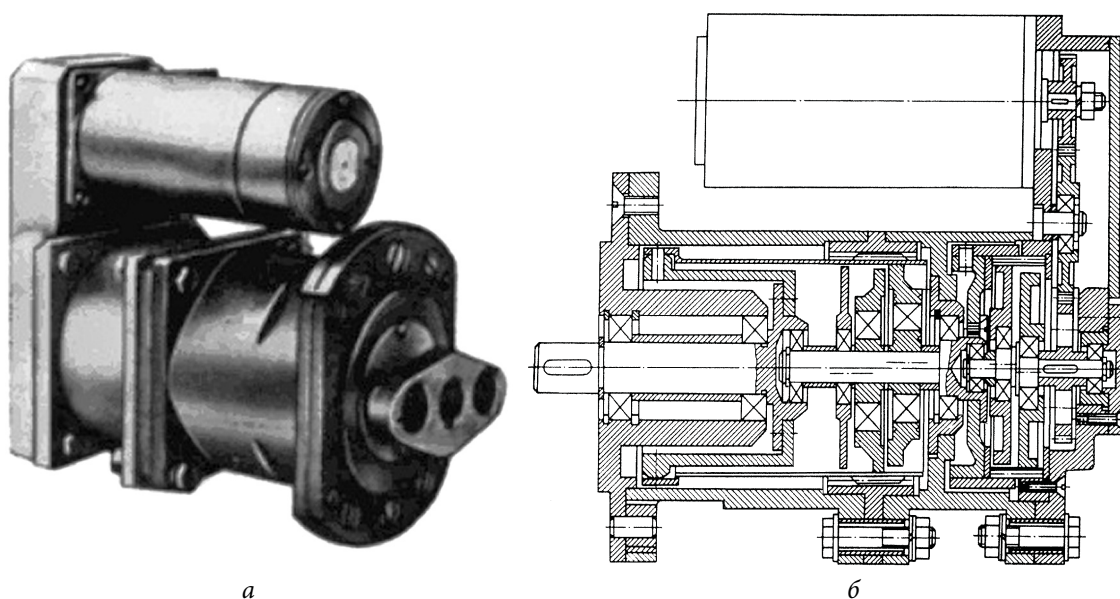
Внешний вид (а) и конструктивная схема (б) силового привода с двухступенчатой волновой передачей
